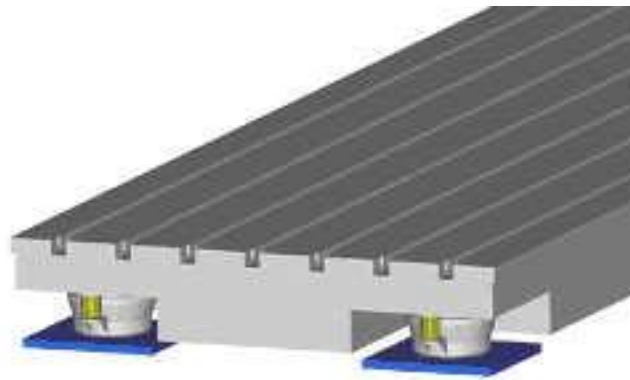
Carga máxima para el cálculo de la base de hormigón
